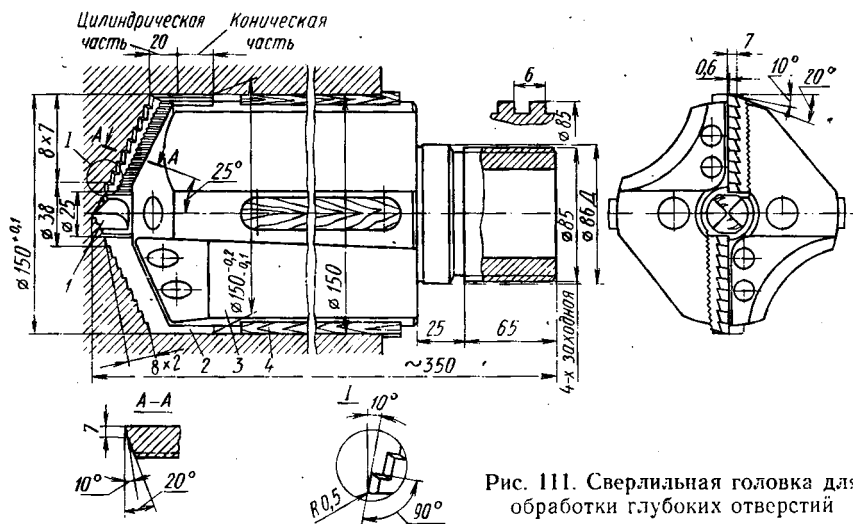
Сверлильная головка для обработки глубоких отверстий
